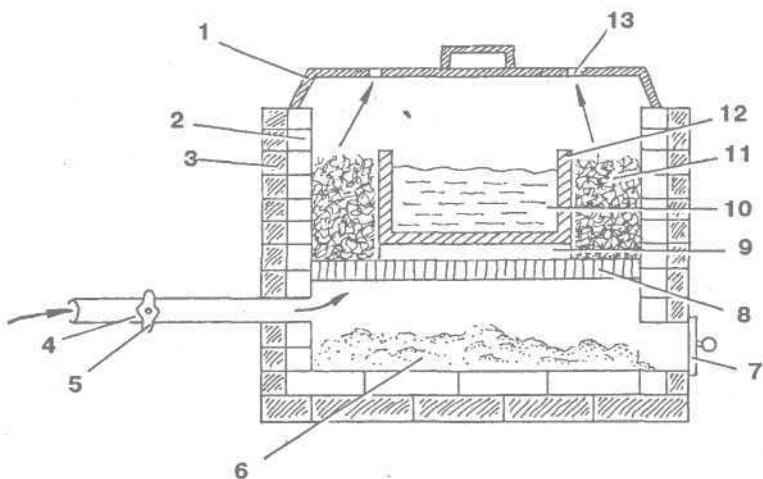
Шахтастиглем в разрезе: 1 — крышка; 2, 3 — стенки горна: внутренняя из огнеупоров и внешняя из обычного кирпича; 4 — подача воздуха; 5 — регулятор подачи воздуха; 6 — зольная камера; 7 — заслонка зольника для удаления золы; 8 — колосниковая решетка; 9 — подставка под тигель; 10 — металл; 11 — топливо; 12 — тигель; 13 — отверстия для выхода газов горения
